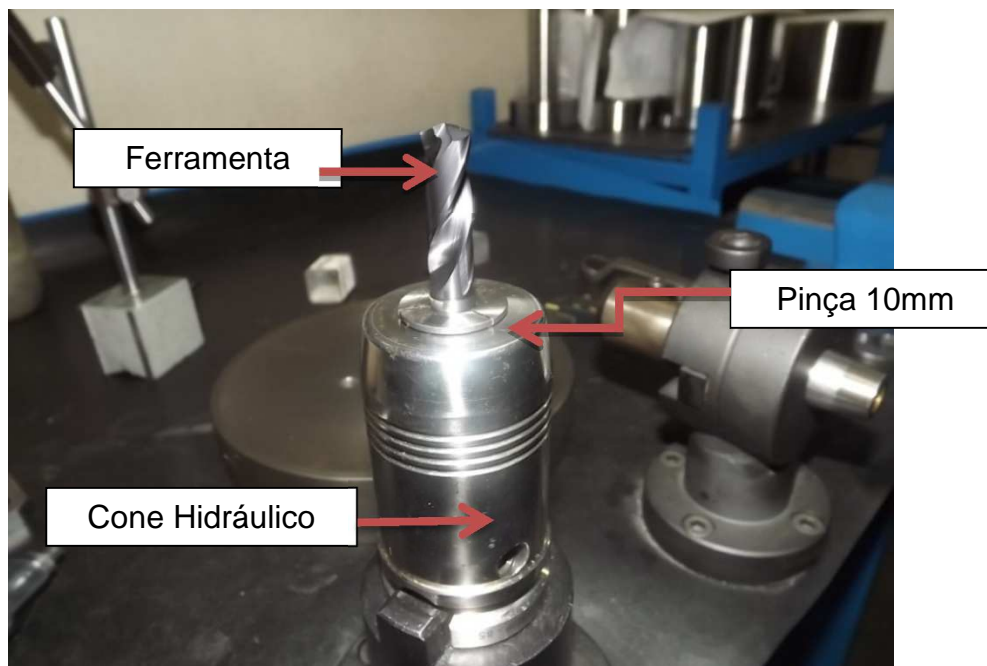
Mandril hidráulico com fixação para diâmetro 10mm
